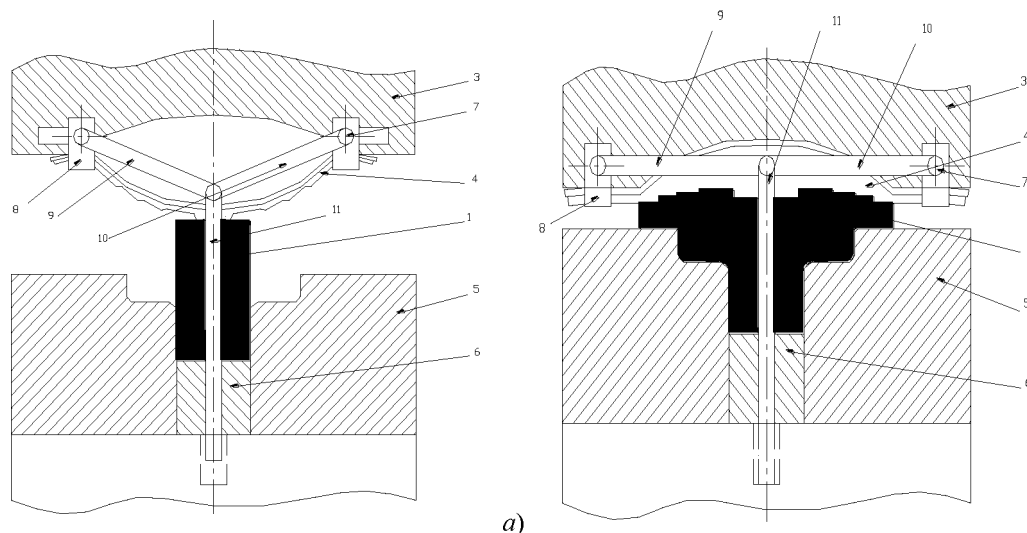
инструмент с изменяющейся формой рабочей поверхности до (а) и после (б) выполнения операции штамповки
